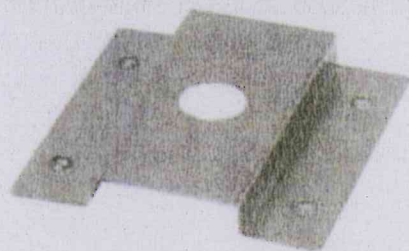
Konstrukcja wsporcza paneli pv - przykład.
